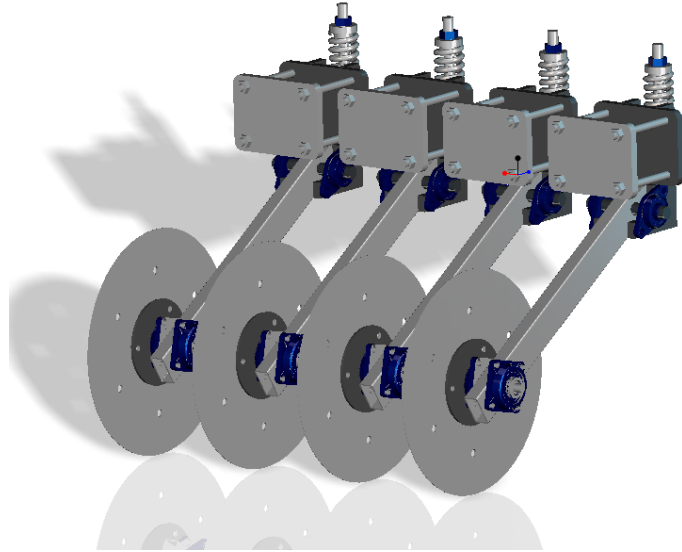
Diseño en Pro-E del mecanismo de control de profundidad del carro-portasensores.
